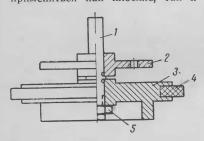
Конструкция подающего узла с подшипником скольжения.
